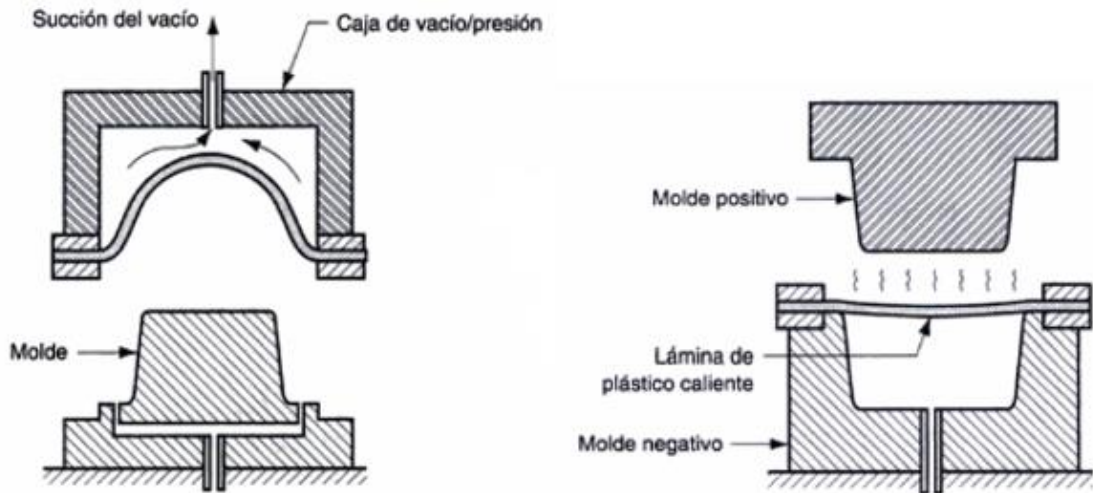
Proceso termoformado a presión utilizando molde negativo [17].
